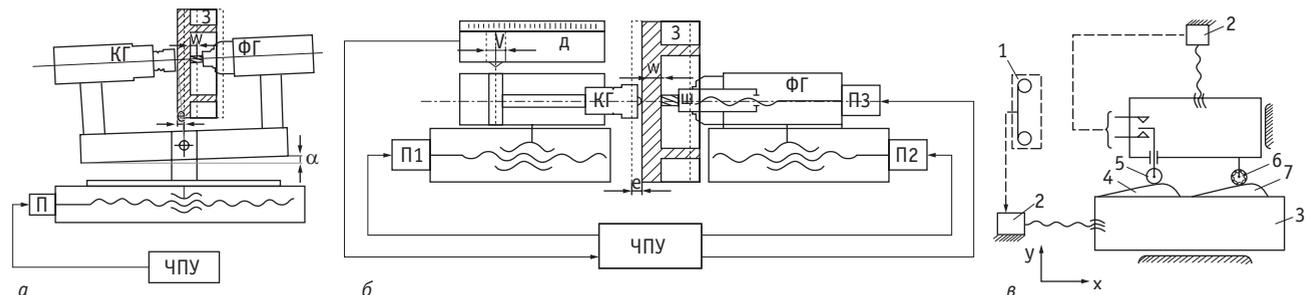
Различные схемы программно-копировальных фрезерных станков: а – с механическим (силовым) копированием одной из поверхностей обрабатываемой детали, б – с электромеханическим копированием одной из поверхностей обрабатываемой детали, в – с копиром, установленным рядом с обрабатываемой деталью
